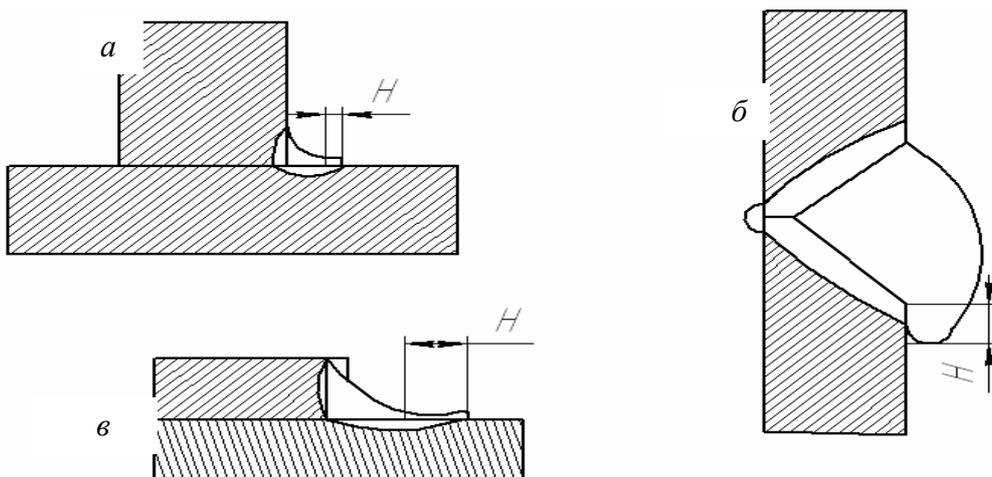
Наплыв сварного шва: *a* – таврового; *б* – стыкового; *в* – нахлесточного
